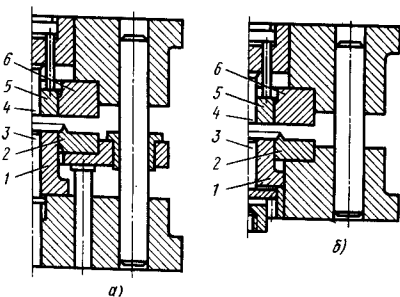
Схемы конструкций штампов для чистой вырубке—пробивки:
